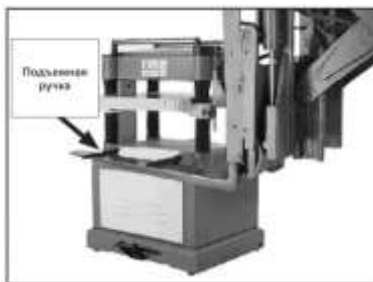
Подъем рейсмусового станка вилочным погрузчиком
